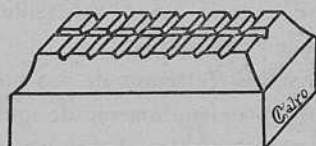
Ranurado de una superficie que se ha de soldar con placa.
